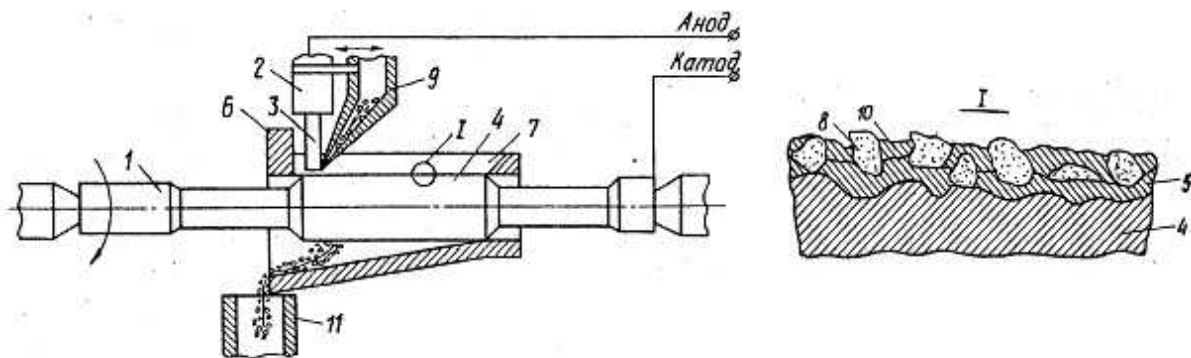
Технологическая оснастка для изготовления притиров для доводки глубоких прецизионных отверстий: 1 – корпус притира; 2 – искровое устройство; 3 – электрод; 4 – рабочая поверхность притира; 5 – слой меди (первичный); 6 – обечайка; 7 – прорезь; 8 – абразивные частицы; 9 – подающее устройство; 10 – слой меди (вторичный); 11 – накопитель
